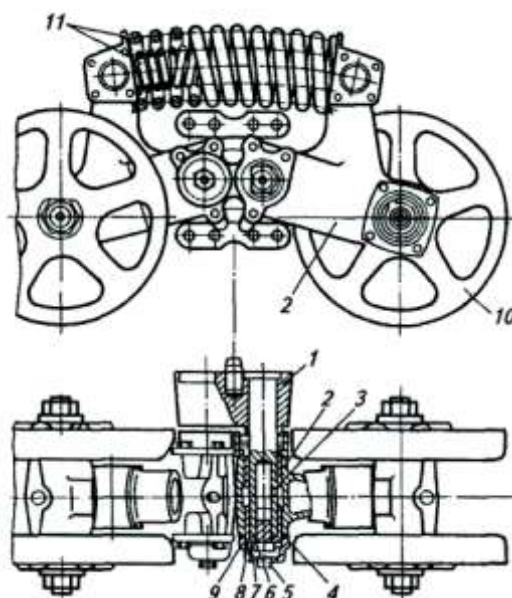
Каретка подвески трактора ХТЗ-150-09
